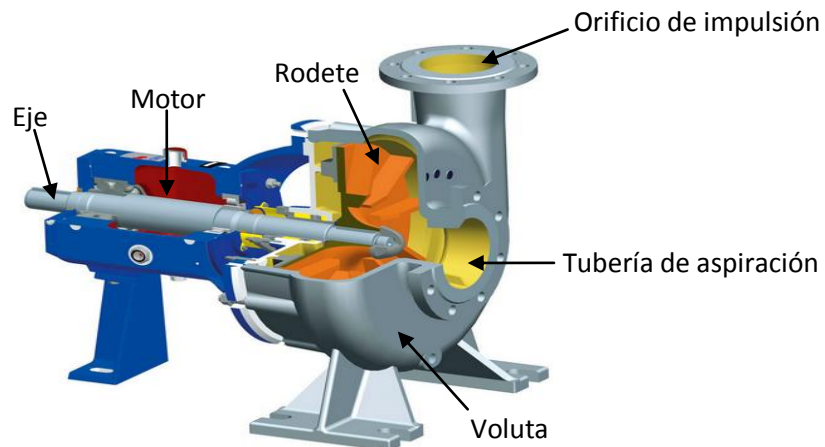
Componentes internos de una bomba horizontal centrífuga
